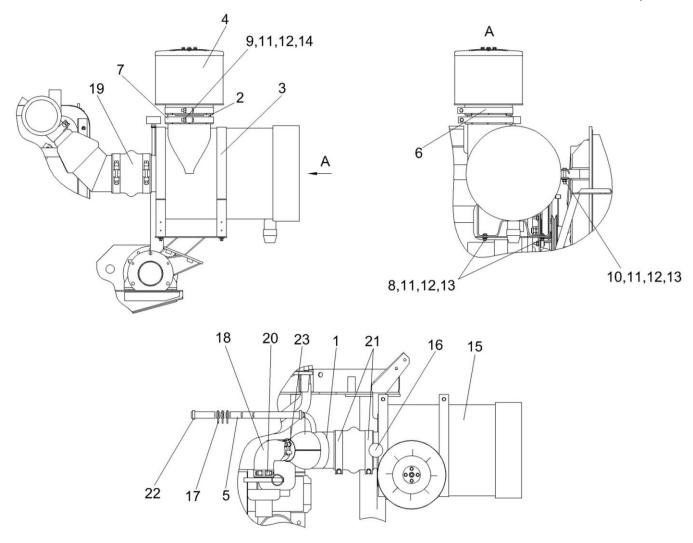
Установка воздухоочистителя КЗК-812С-0106080
